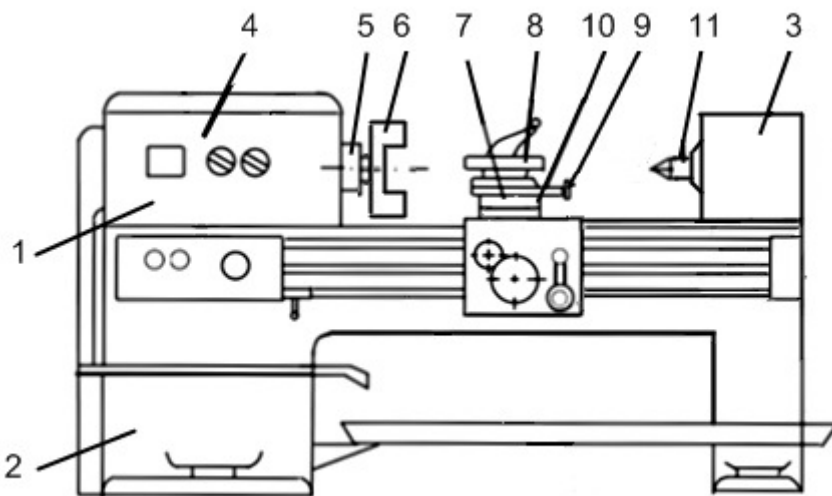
Загальний вигляд токарно-лобового верстату
